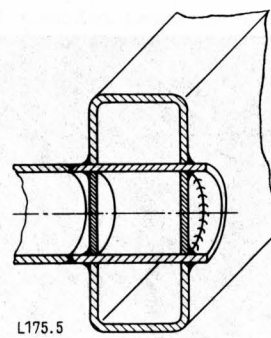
Ausführung für durchgehenden Querträger; Rohr außerhalb des Kastenprofils verschweißt.
